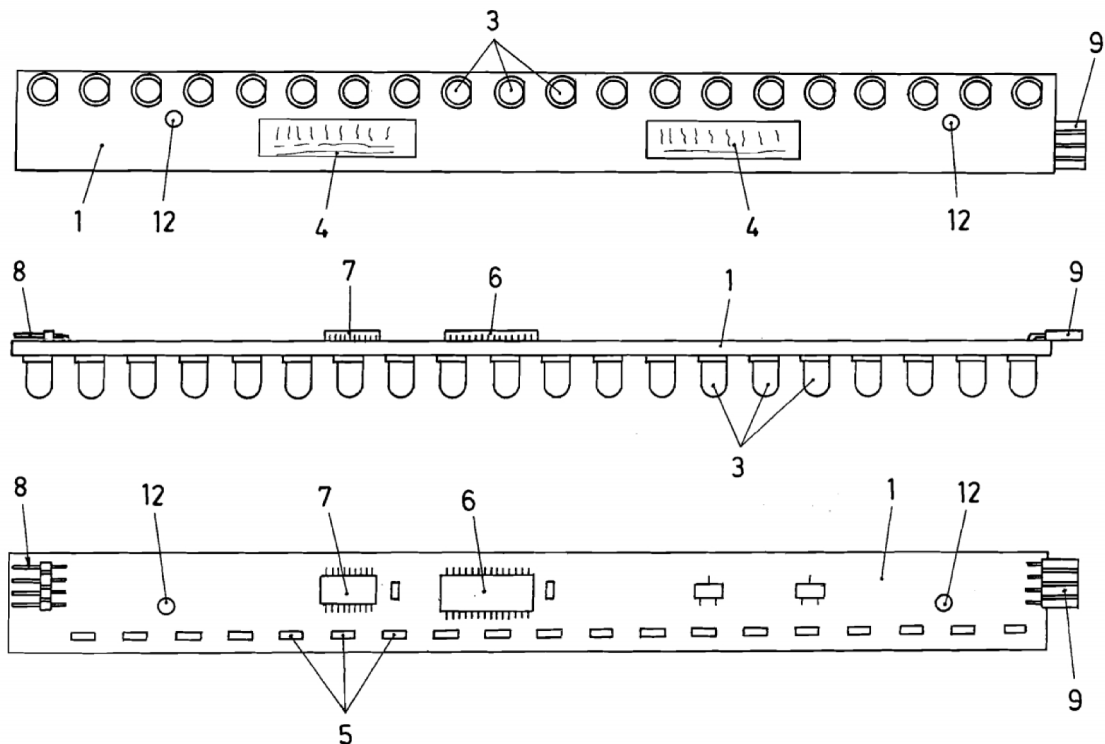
Vista frontal, vista en planta y vista posterior de un microservidor con formato de tira de leds modular.
